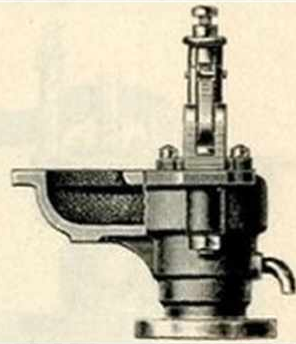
et 22a: tubulure de dégagement latéral à bride horizontale. La tubulure peut se trouver à droite, à gauche ou à l'arrière du levier.
